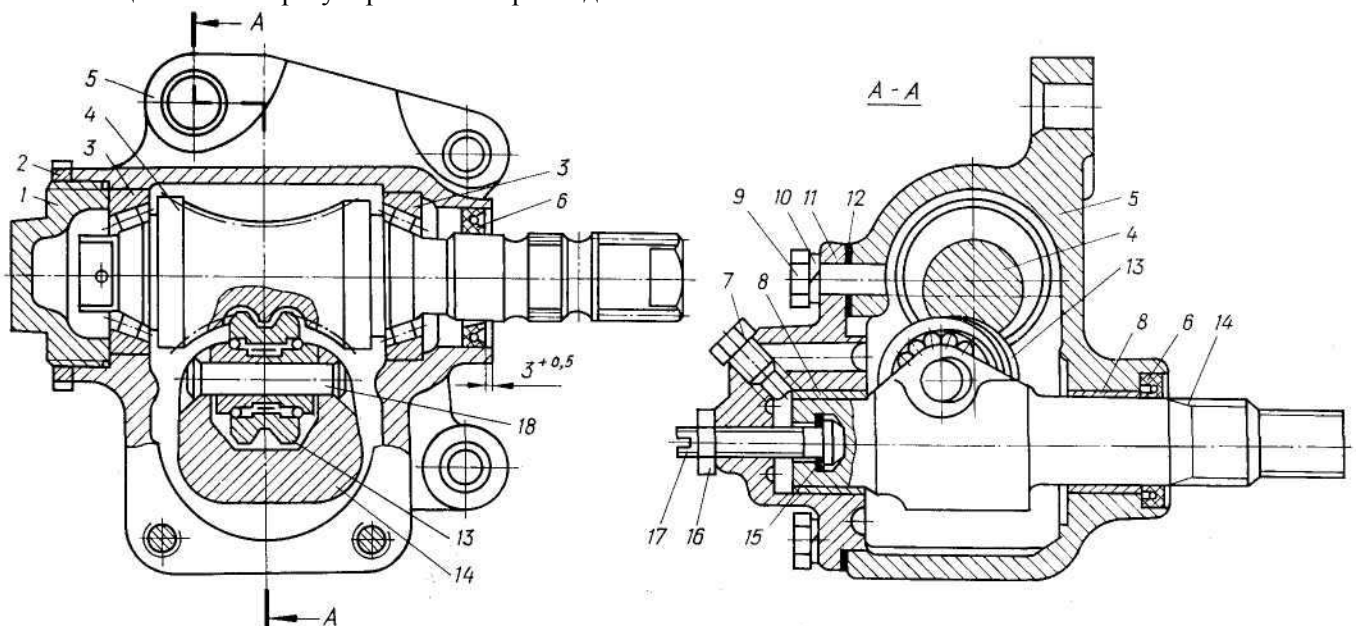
Механизм рулевой (без вала, опоры вала и рулевого колеса):
